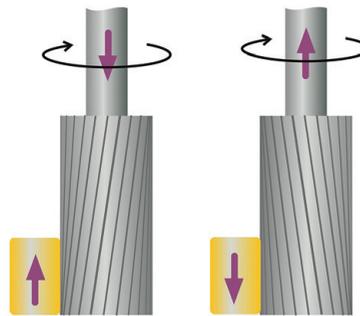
Beim rechtsgewundenen Werkzeug wird das Werkstück aus der Halterung herausgezogen. Beim linksgewundenen Werkzeug wird das Werkstück in die Halterung und gleichzeitig das Werkzeug in die Spannzone hineingedrückt.
